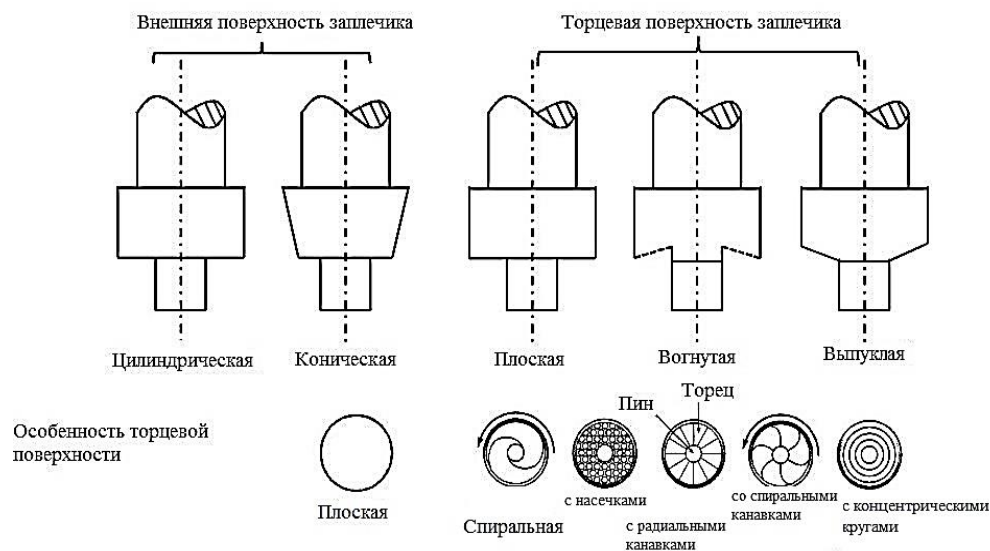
Основные виды форм заплечика инструмента для сварки трением с перемешиванием
